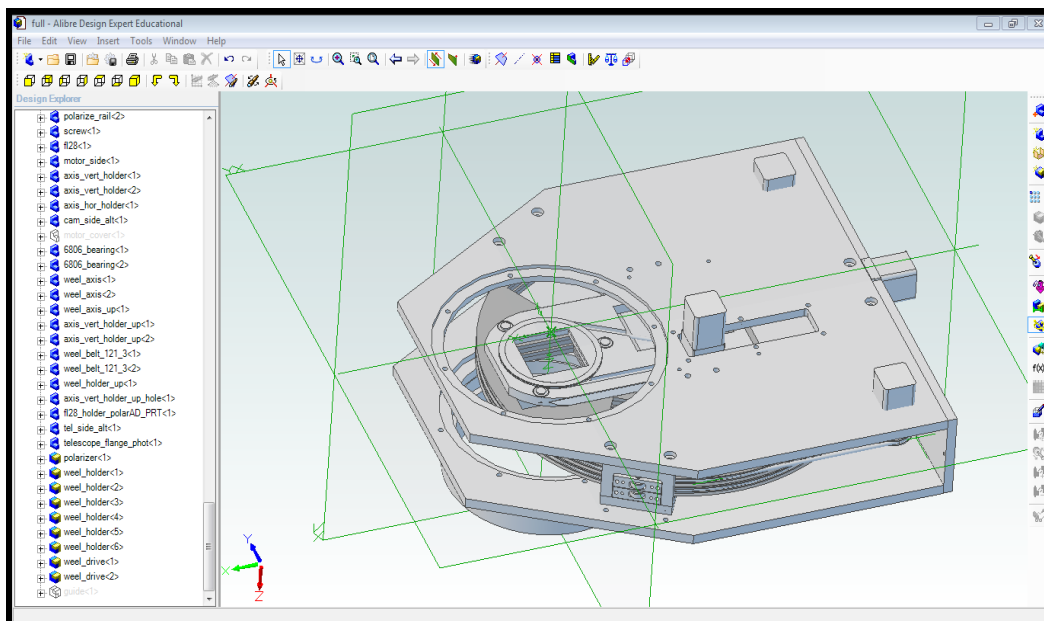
Общий вид прибора, часть элементов конструкции не показана.
